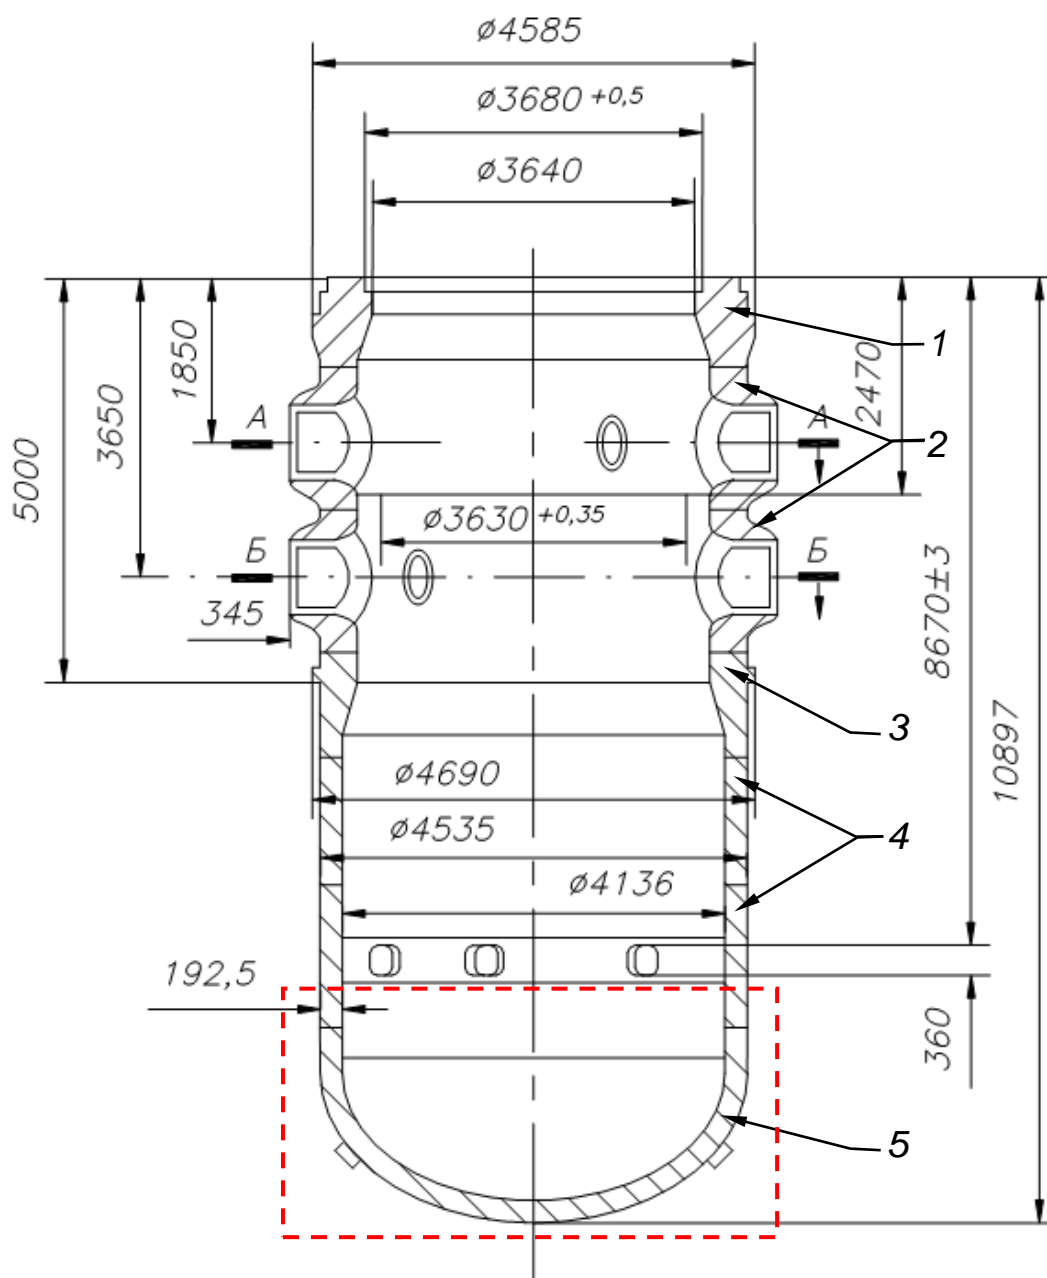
Корпус реактора ВВЭР-1000 [79]
